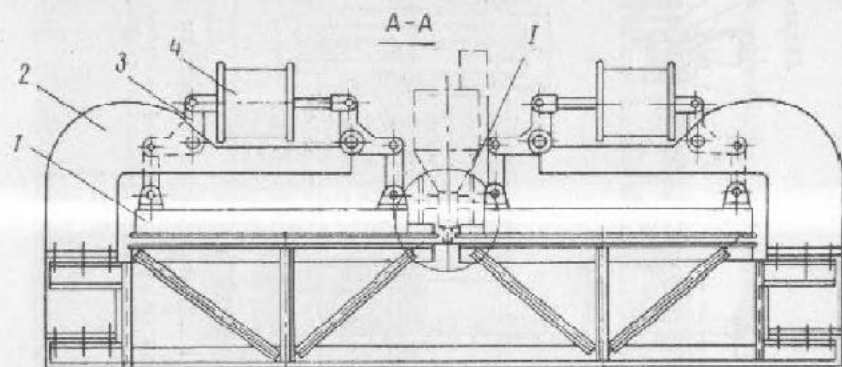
Поперечный разрез стола для сварки пазов полотнищ.
